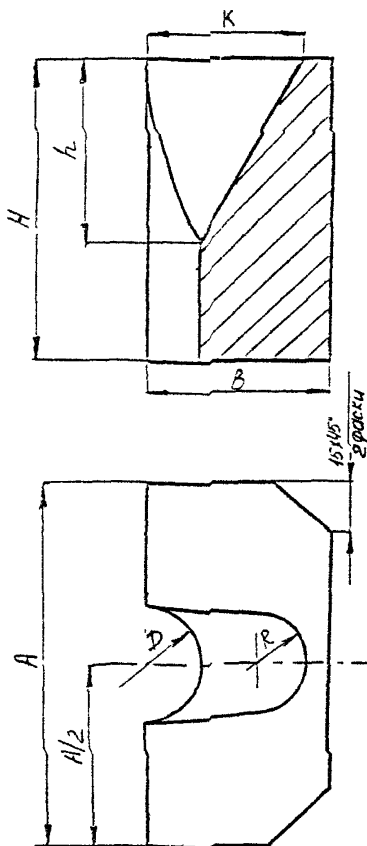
Конструкция инвентарной медной формушей детали для комбинированной сварки стыковых соединений стержней в вертикальном положении
